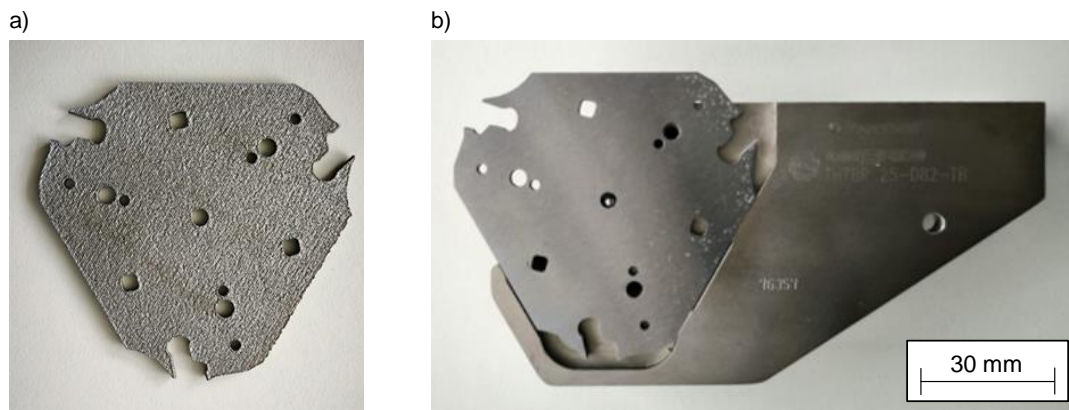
Additiv gefertigter Werkzeughalter; a) ohne Nachbearbeitung; b) mit Nachbearbeitung
